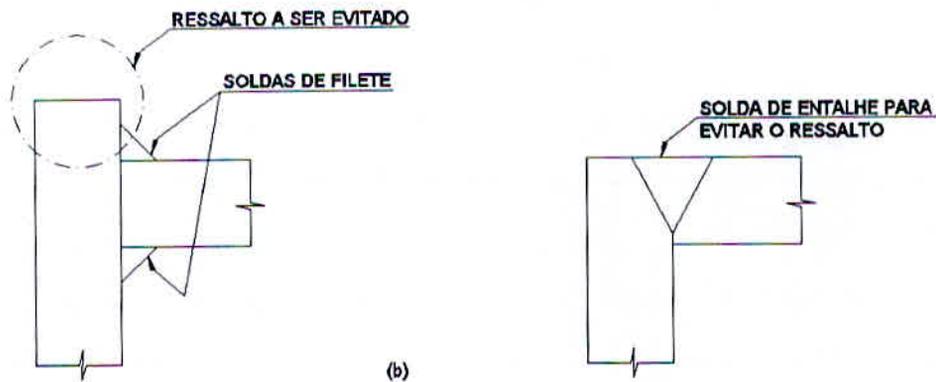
Soldas de Entalhe. Fonte: Autor.
